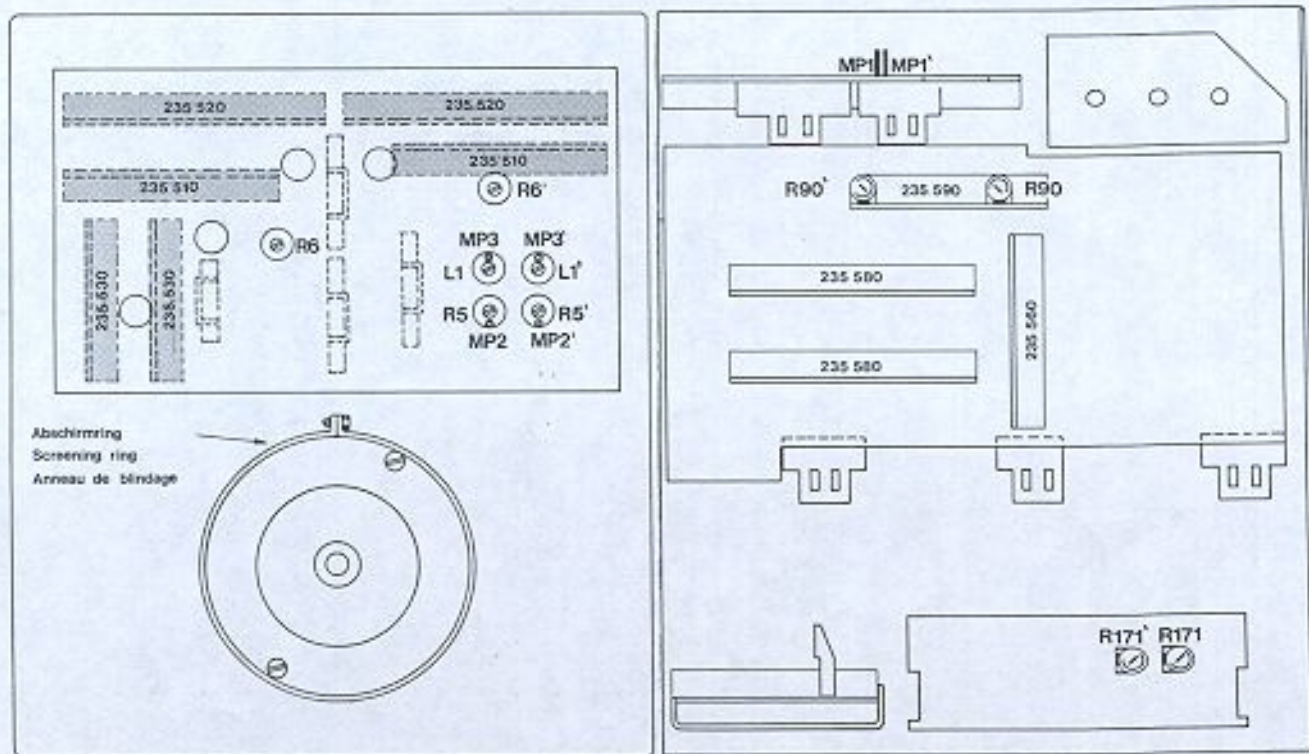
Abgleichpositionen, Geräteunterseite und Lageplan der Module
